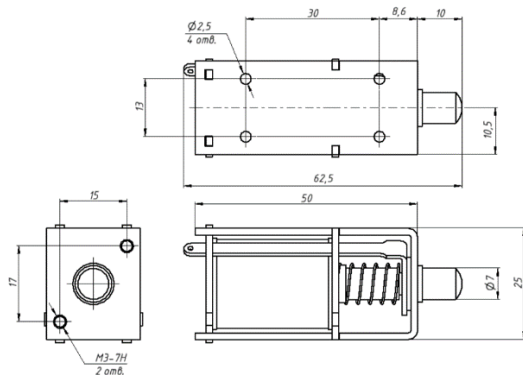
Габаритные и установочные размеры замка серии Promix-SM490
